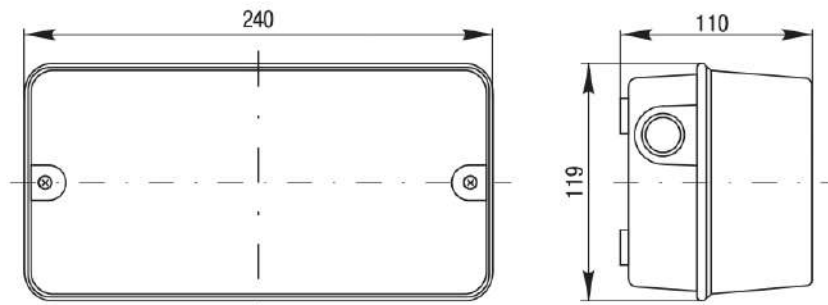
Габаритные и установочные размеры светильника НПП 3006
